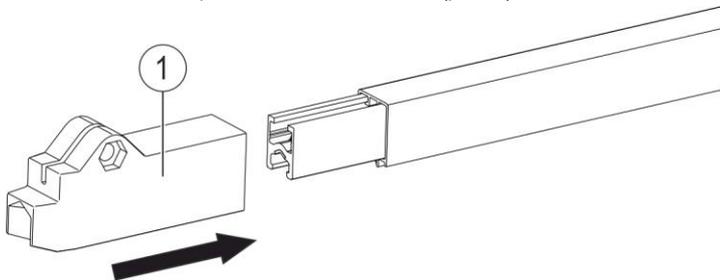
Pousser l'embout final sur l'extrémité du rail
